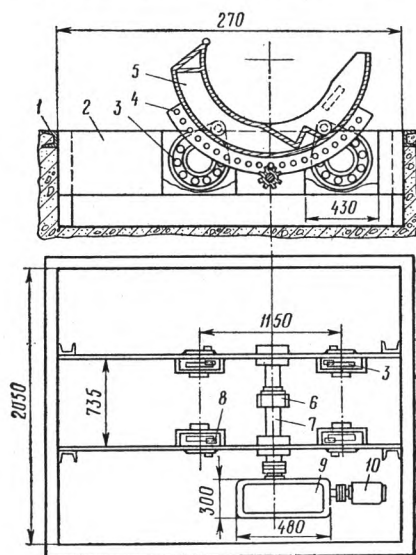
Кантователь для сборки и разборки колесно-моторных блоков:
